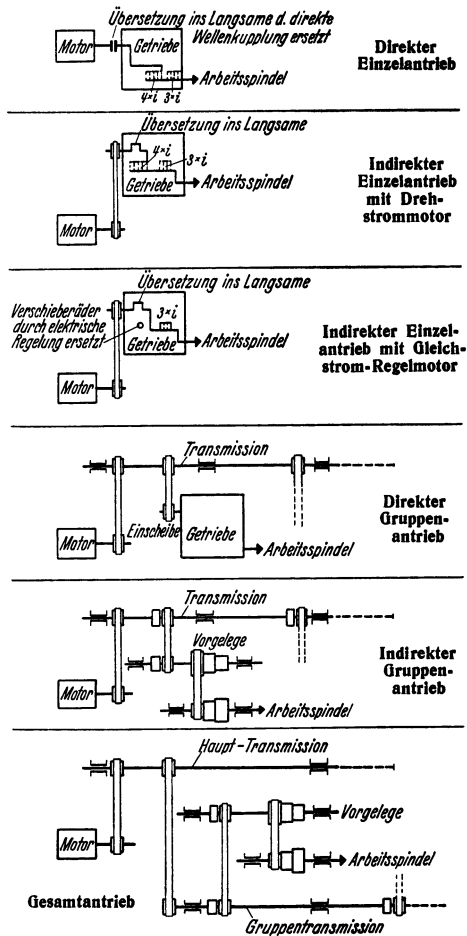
Antriebsarten von Werkzeugmaschinen.
